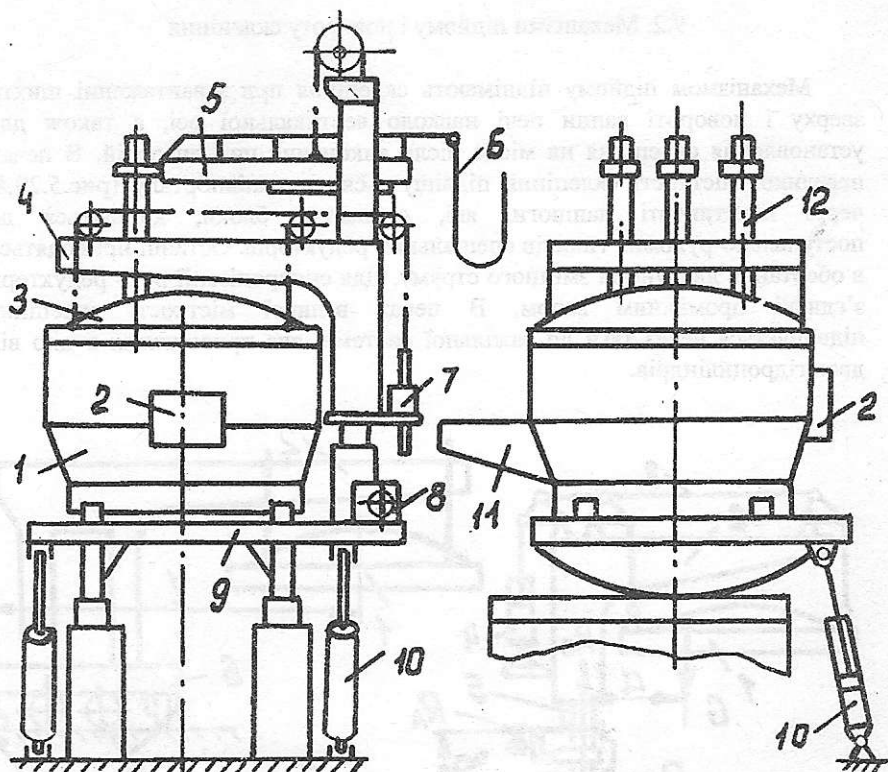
Схема дугової електроплавильної печі: 1-ванна; 2-робоче вікно; 3-склепіння; 4-напівпортал; 5-система переміщення електродів; 6-струмопідвід; 7-привод механізму підйому склепіння; 8-механізм повороту склепіння; 9-люлька; 10-механізм нахилу; 11-зливний носик; 12-електроди
